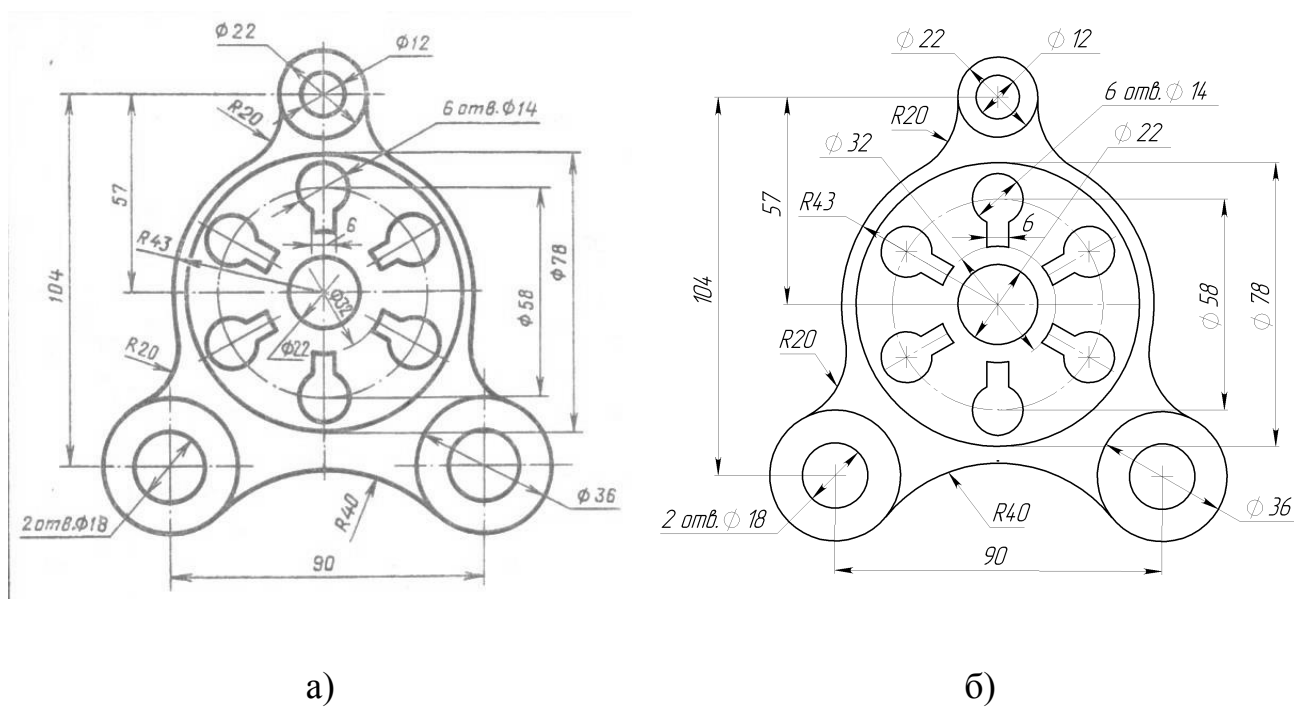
Крышка: а) – задание; б) – готовый эскиз детали
